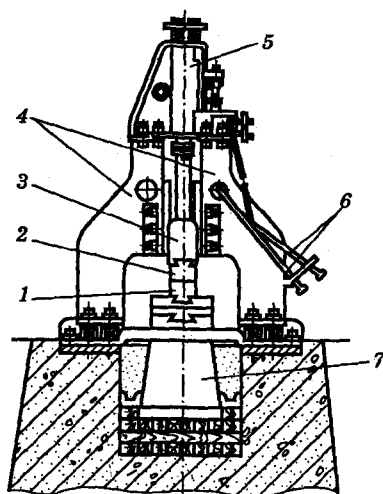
Паровоздушный ковочный молот арочного типа
